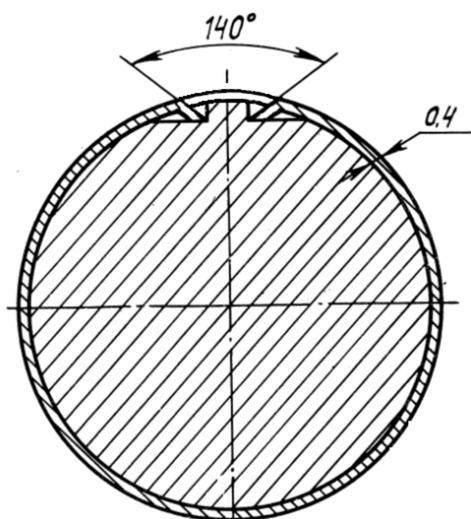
Схема установки упругой ДРД на шейку вала
